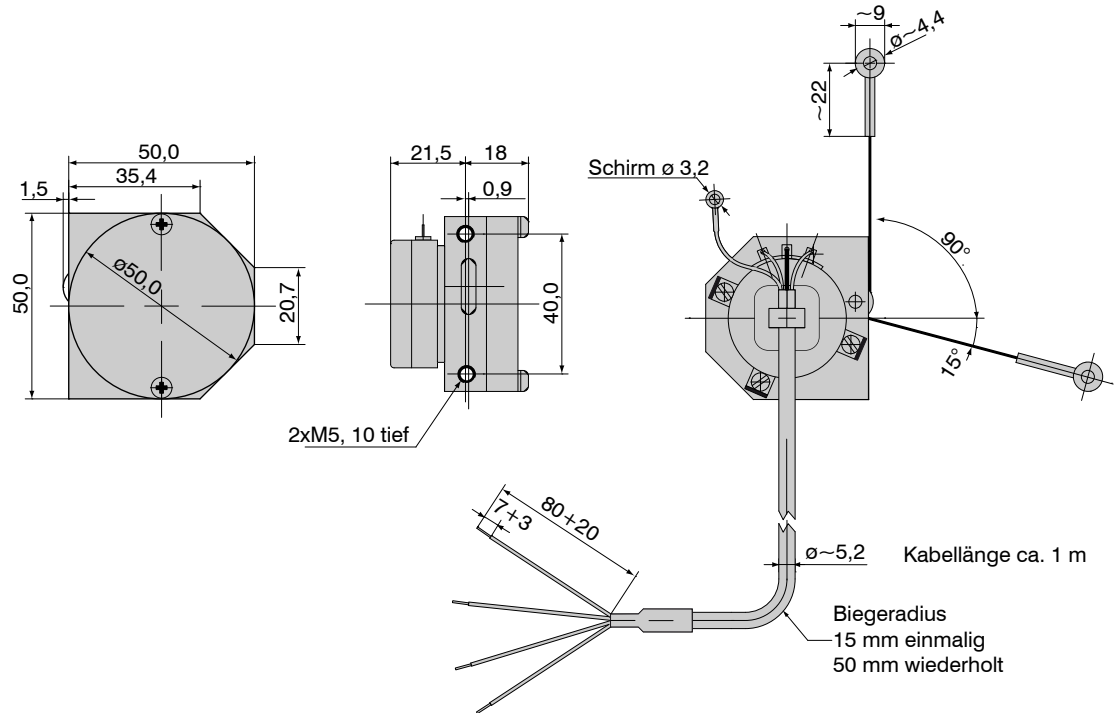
Maßzeichnung WDS-70-F50, mit Potentiometer, Maße in mm, nicht maßstabsgetreu
